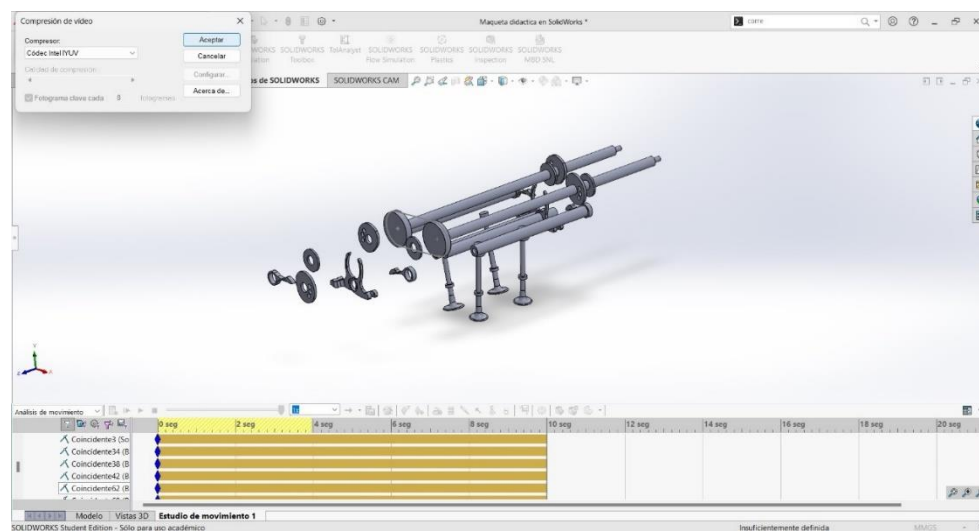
Compresión del video de Explosionado. Fuente: SolidWorks
